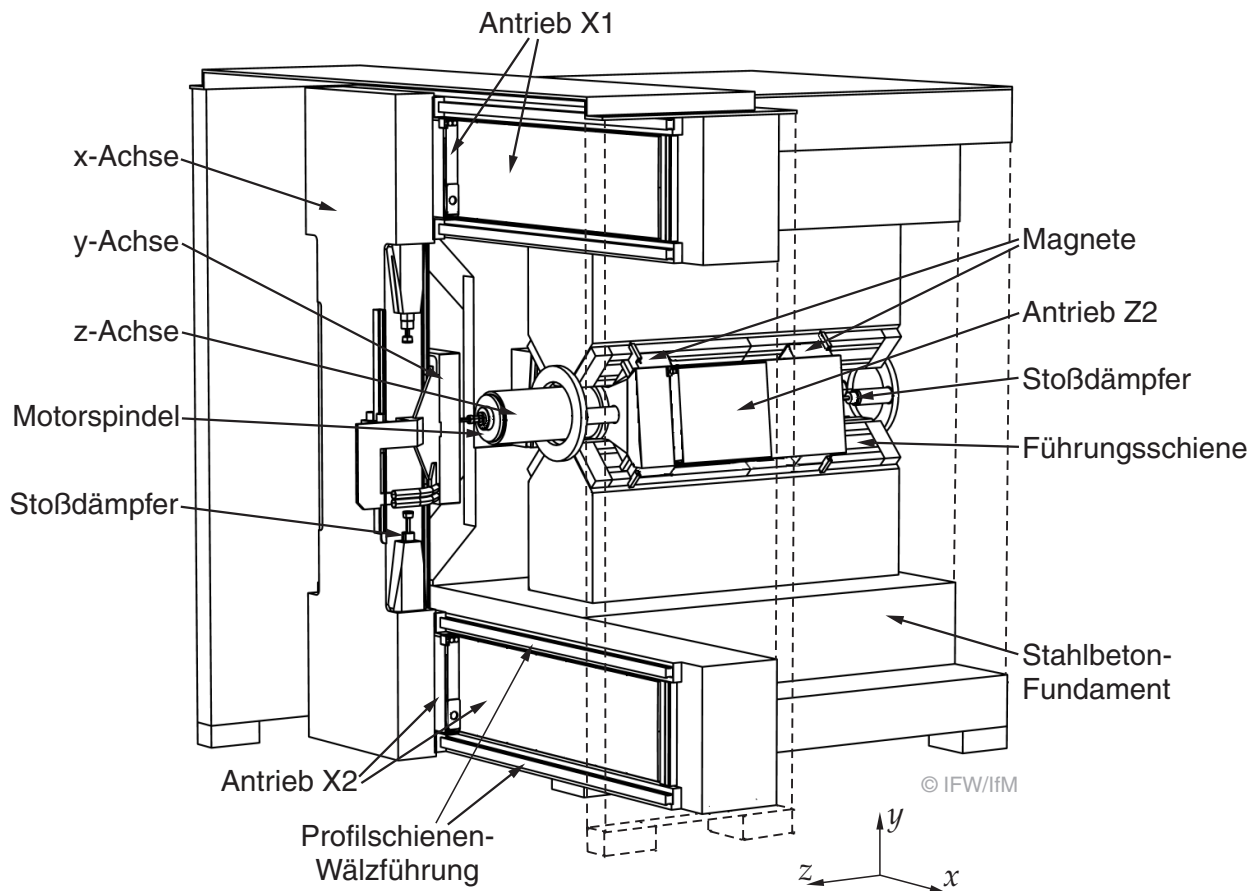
Schematische Ansicht der SCHNELLEN MASCHINE [DENK04b]
